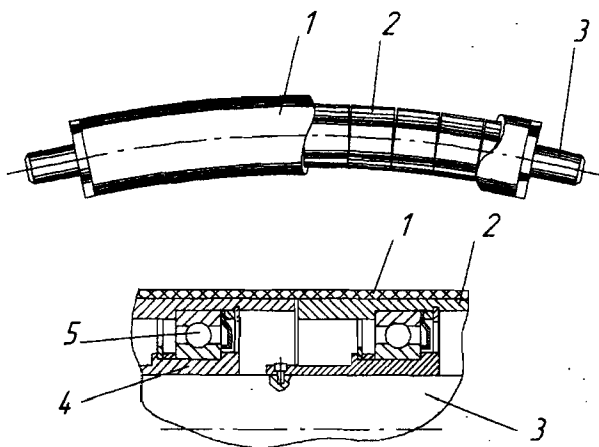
Изогнутый валик Маунт-Хоуп: 1 – рубашка вала; 2 – опорная втулка; 3 – ось вала; 4 втулка; 5 - подшипник
